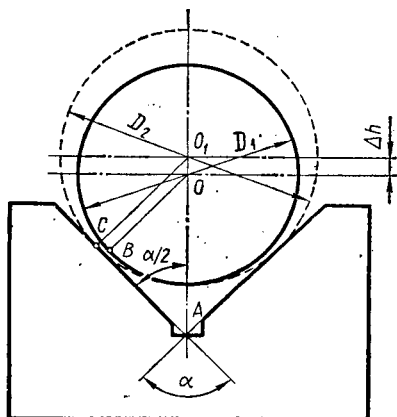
Схема для расчета погрешности базирования вала при установке в призму
